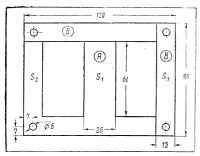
Чертеж пластины сердечника стабилизатора: А — основная пластина; Б — перемычка; В — магнитный шунт
